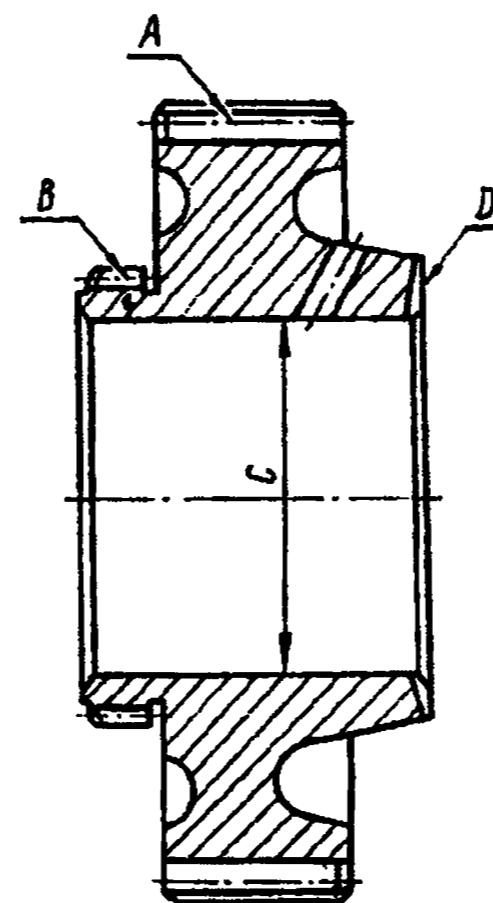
Колесо зубчатое повышающей передачи дифференциала
